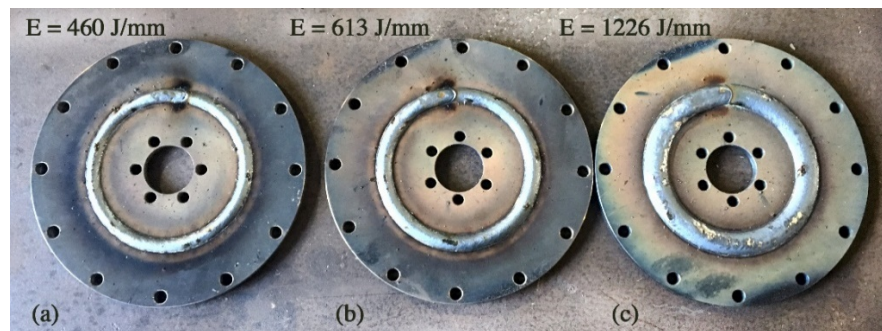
Discos soldados antes de serem usinados: (a) disco 1, (b) disco 2 e (c) disco 3, evidenciando um aumento progressivo no tamanho do cordão de solda do primeiro ao último.
